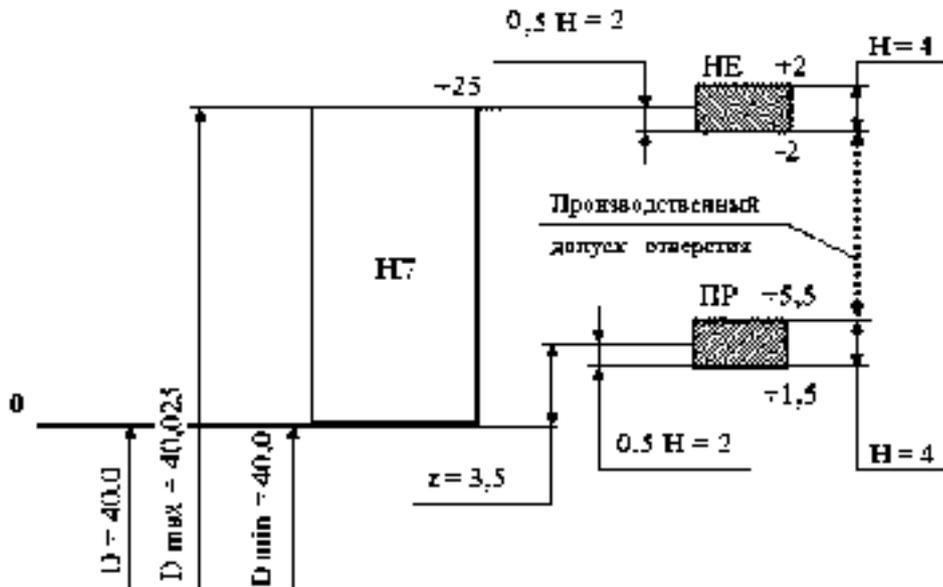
Схема расположения полей допусков на изготовление калибра - пробки для контроля отверстия $\varnothing 40 H7^{(+0,025)}$
